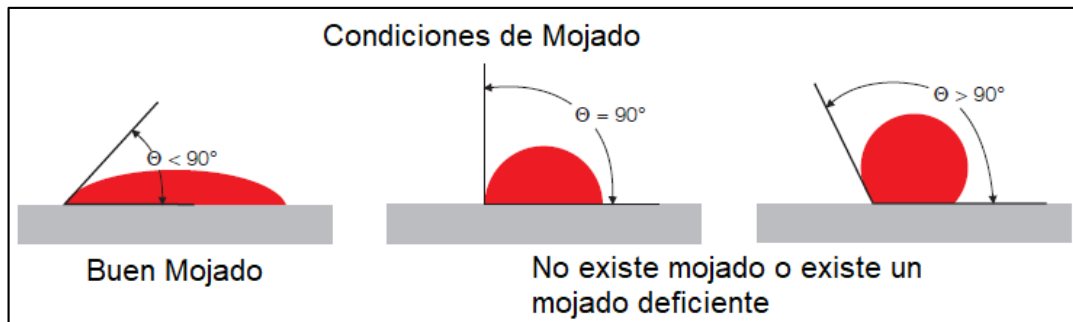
Incidencia del ángulo de contacto de mojado de un metal de aporte en soldadura indirecta.
